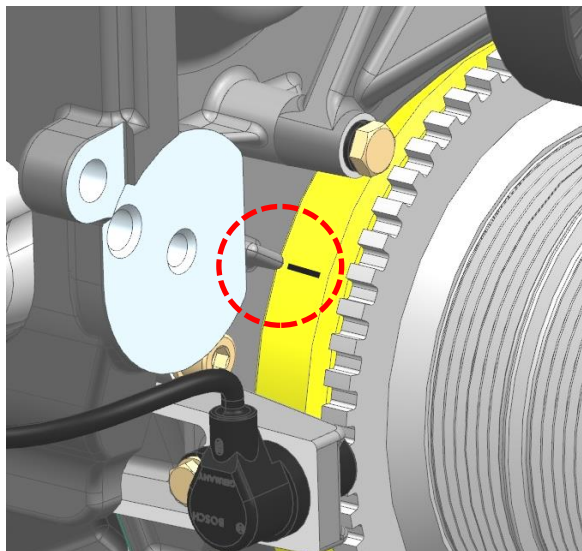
Риска на шкиве коленчатого вала и указатель на крышке цепи
